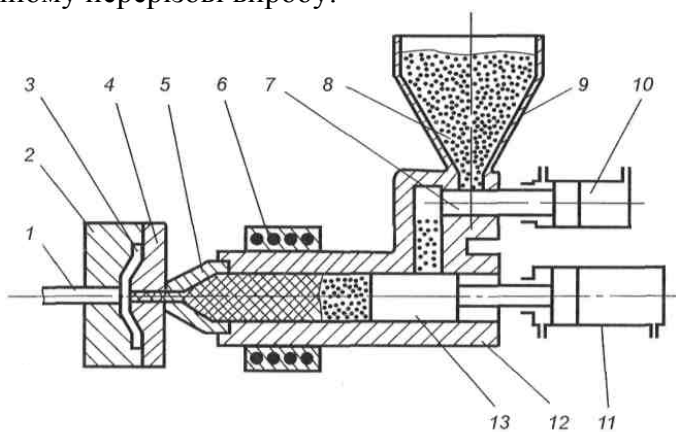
Схема лиття під тиском: 1 – виштовхувач; 2 – рухома половина прес-форми; 3 – деталь; 4 – нерухома половина прес-форми; 5 – сопло; 6 – електронагрівач; 7, 13 – плунжер; 8 – полімерна суміш; 9 – бункер; 10, 11 – привідний циліндр; 12 – робочий циліндр
